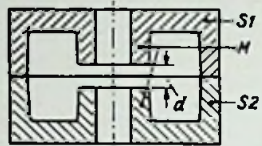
Schnitt durch einen Ferroxcube-Schalenkern. In der Mitte befindet sich ohne Bohrung für den Abgleichstift
